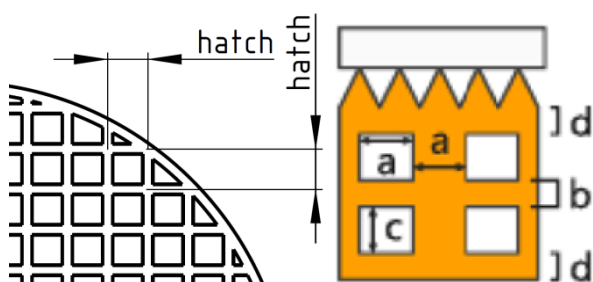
Detail části vzorku ve formátu .STL
